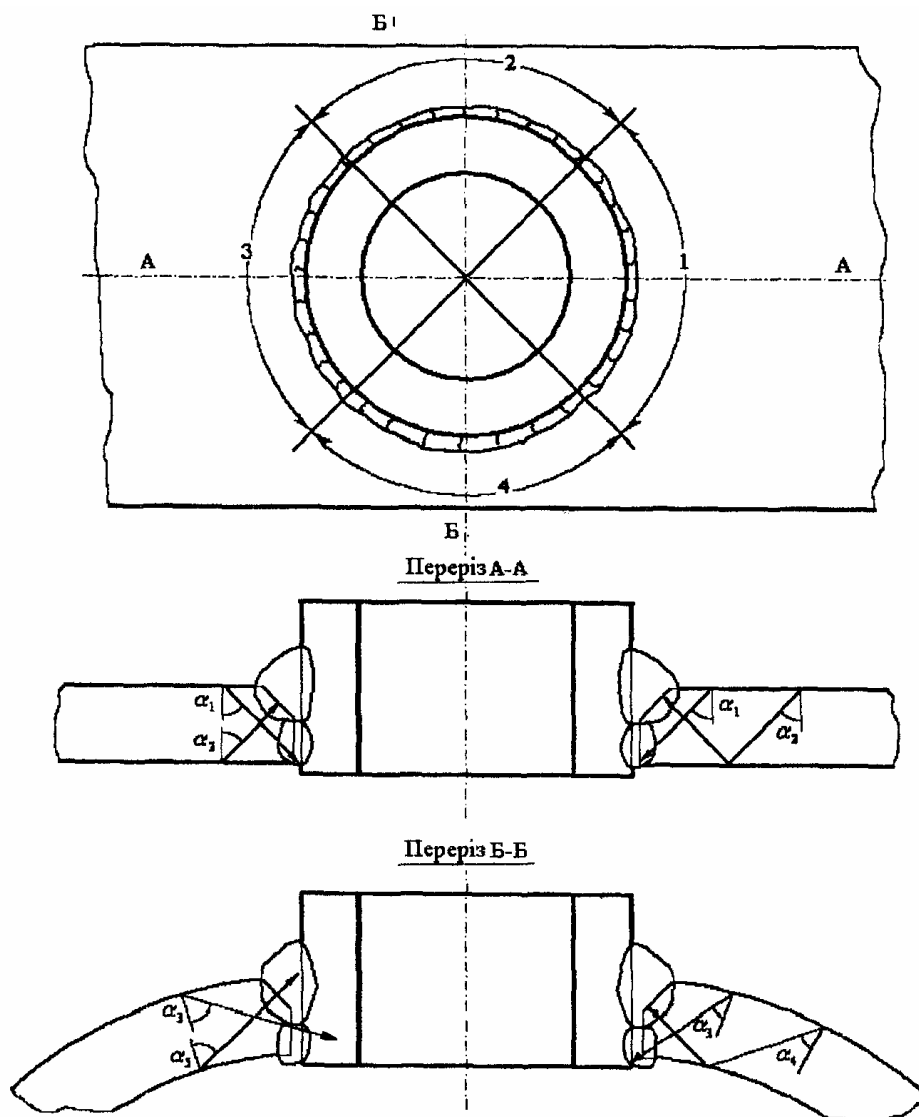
Схема розмічування и контроля углового сварного соединения по поверхности корпуса диаметром 400-800 мм
